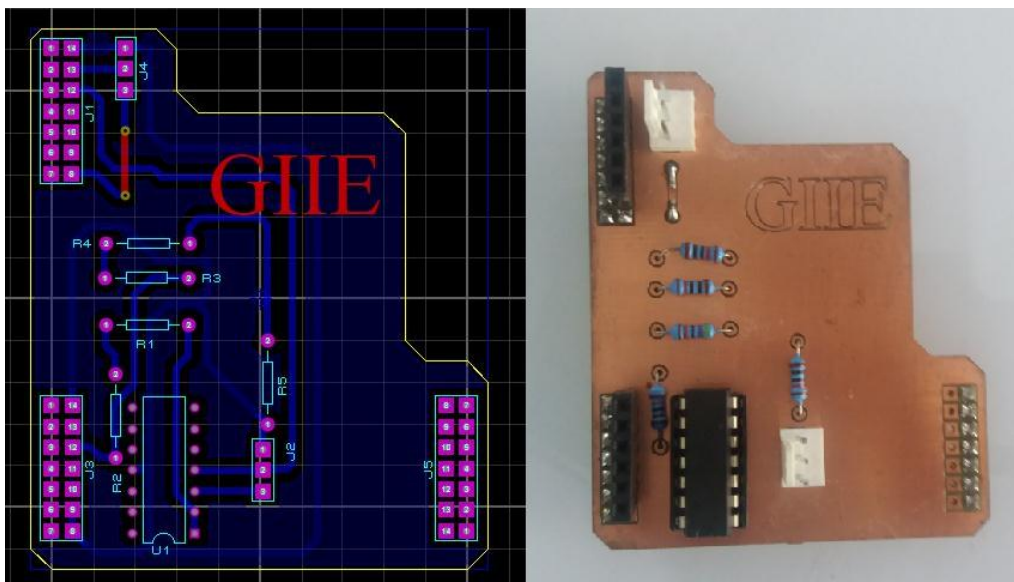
Circuito de acondicionamiento para el sensor SEN0114 montado en PCB con conectores para la *BeagleBone Black* y el sensor DHT22.
